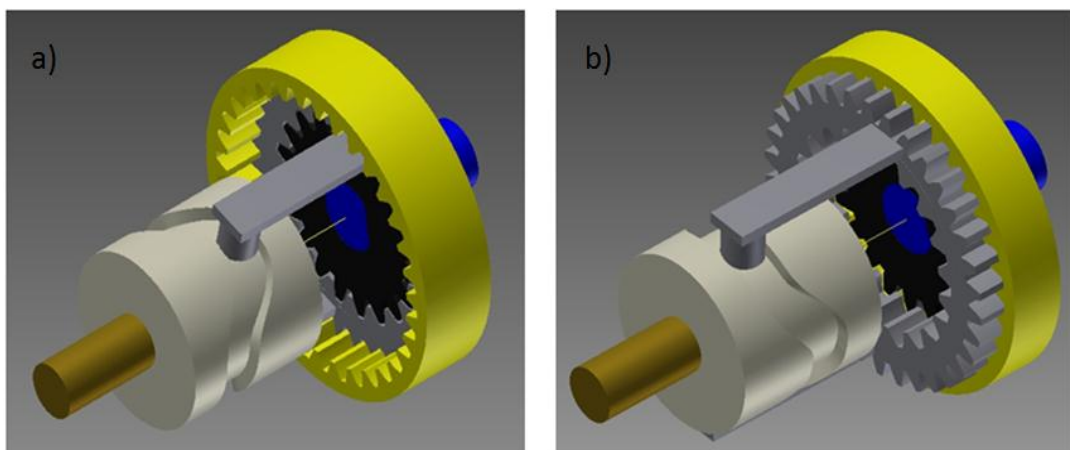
Leva cilíndrica. a) Engrane móvil en posición inicial b) Engrane móvil desplazado
